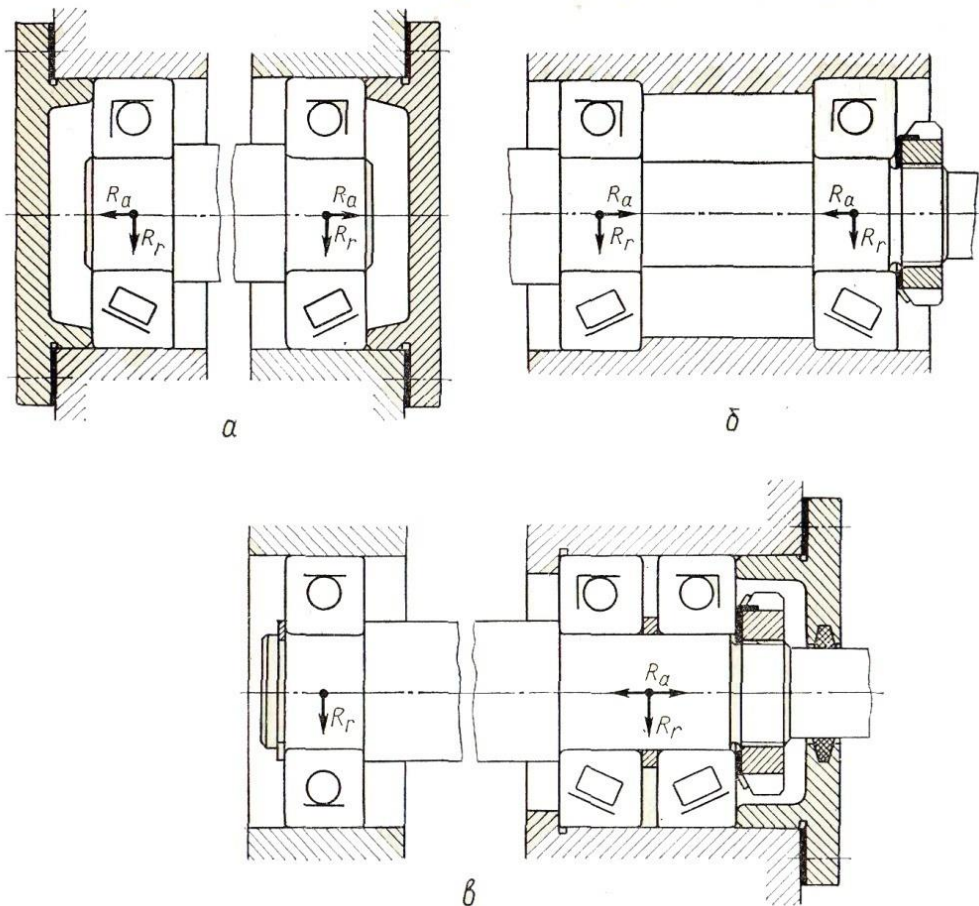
Конструкції опор валів на радіально-упорних підшипниках
